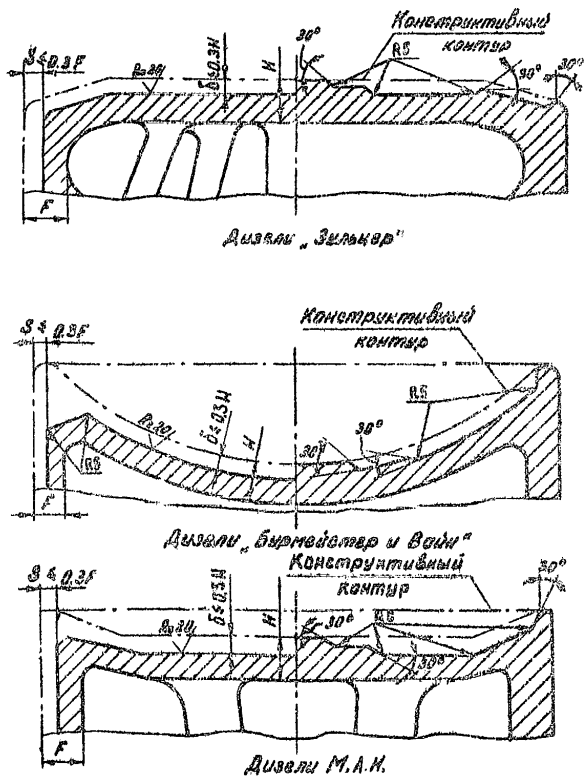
Подготовка дна и наружной цилиндрической поверхности головки поршня к восстановлению
